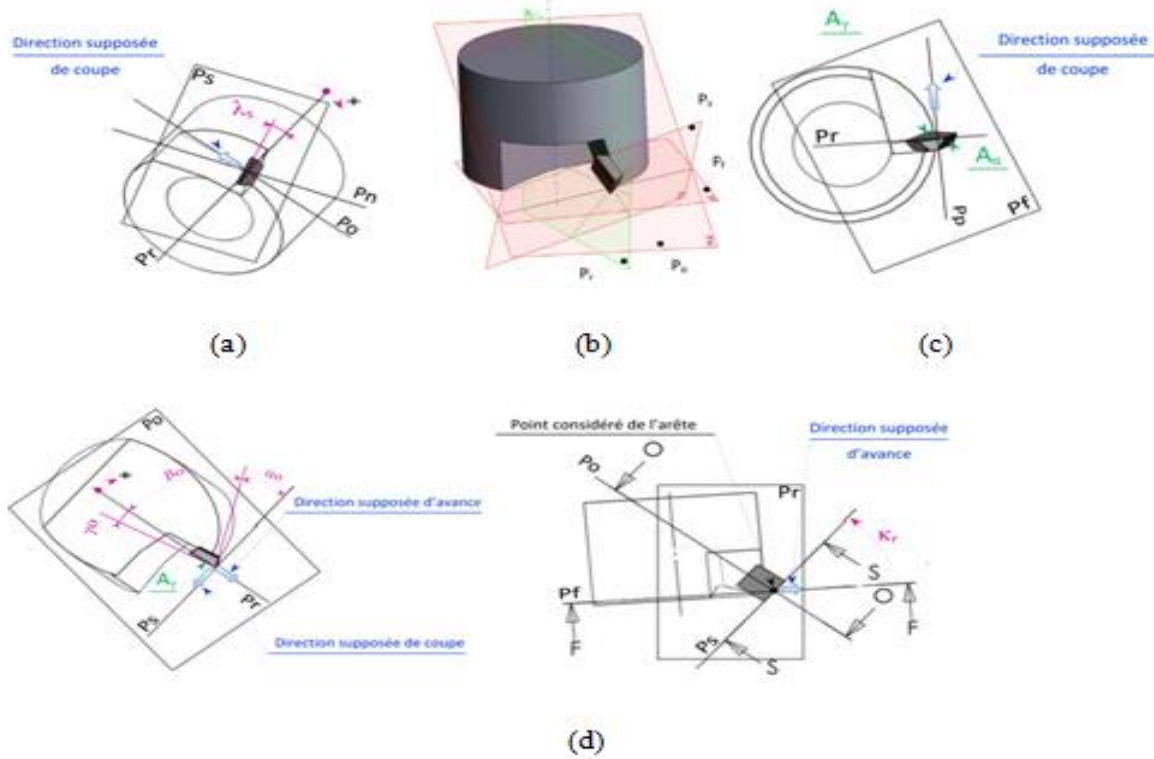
Illustration des plans et angles en main d'une fraise.
